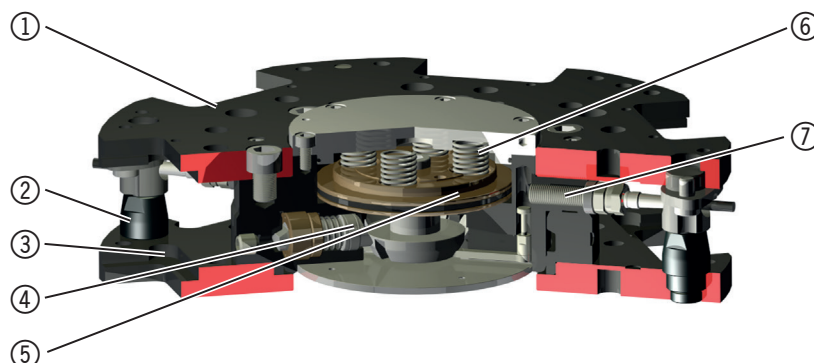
Werkzeugwechsler WWR1000 im Schnitt
